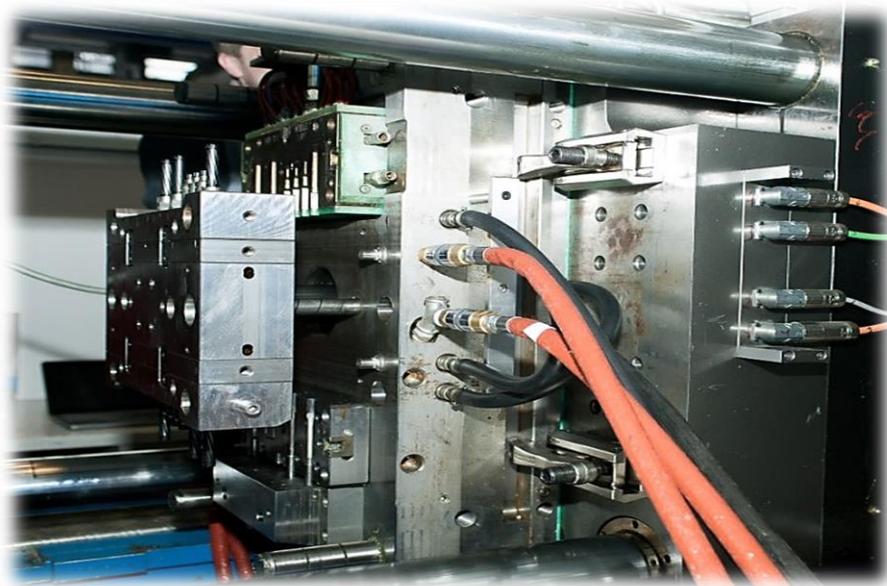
Molde bimatéria - rotação de um inserto do molde
